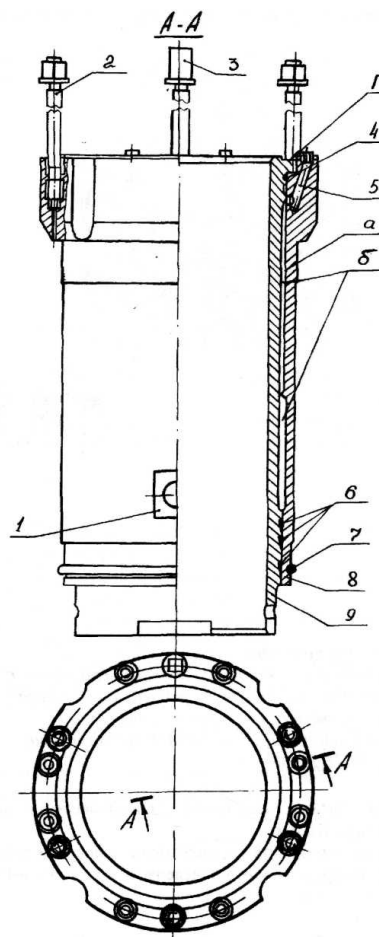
Втулка циліндра з сорочкою: 1 - фланець; 2 - шпилька; 3 - гайка; 4,6,7 - ущільнюючі кільця; 5 - перепускний отвір; 8 - сорочка; 9 - гільза; а - ребро; а - подовжні ребра; б - порожнина охолодження
